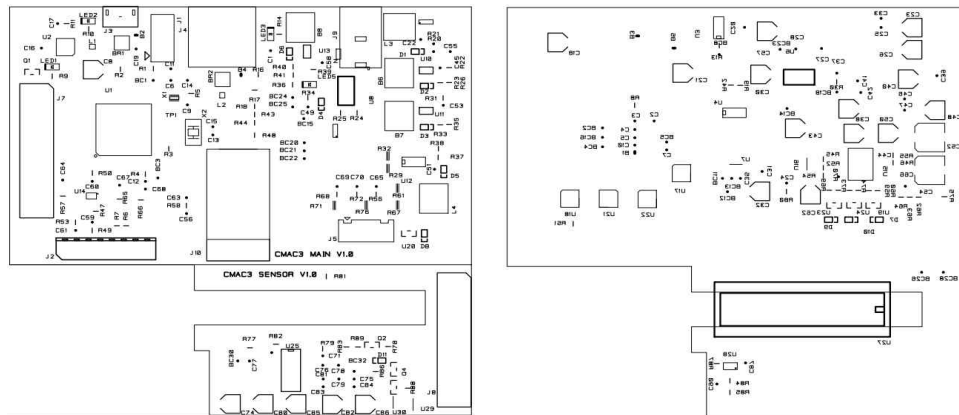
Top(좌) & Bottom(우) Silk layer 회로도에 대한 Drawing 이미지
